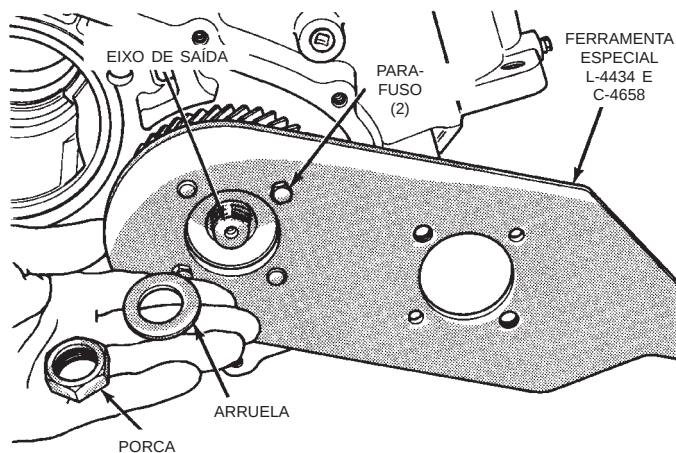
Manutenção da Engrenagem do Eixo de Saída
